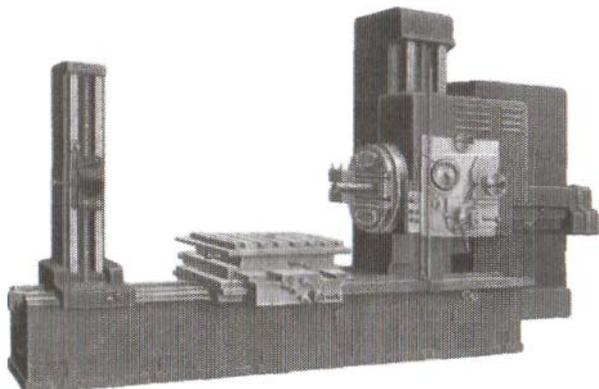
Общий вид горизонтально-расточного станка модели 262Г
